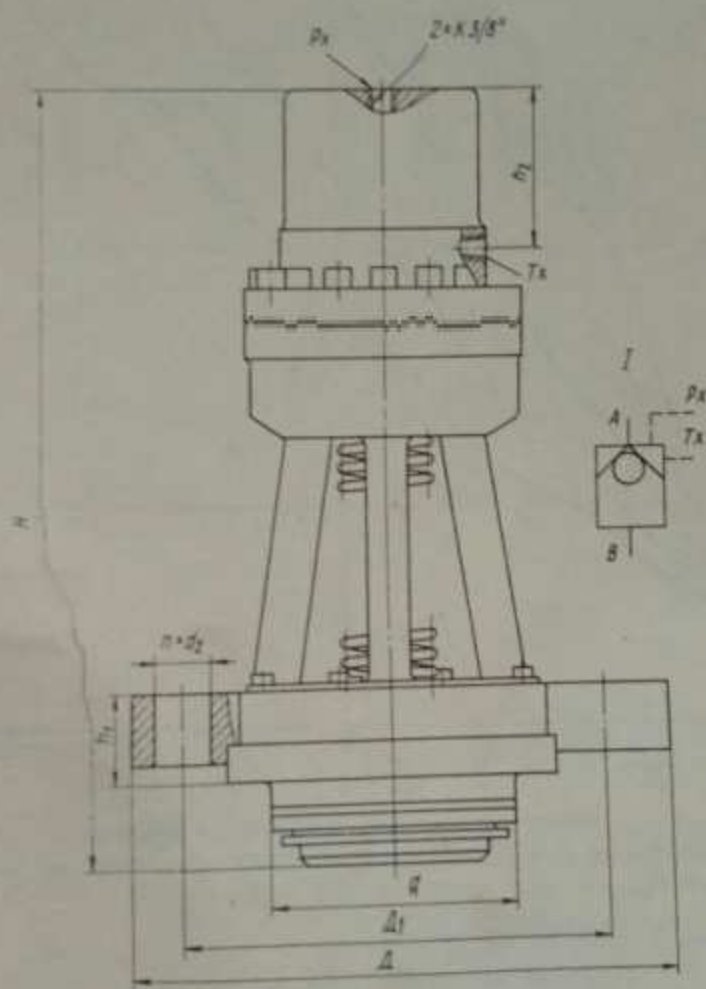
Габаритные и присоединительные размеры гидроэластичных наполнений ИЭН, ИЭКН:
